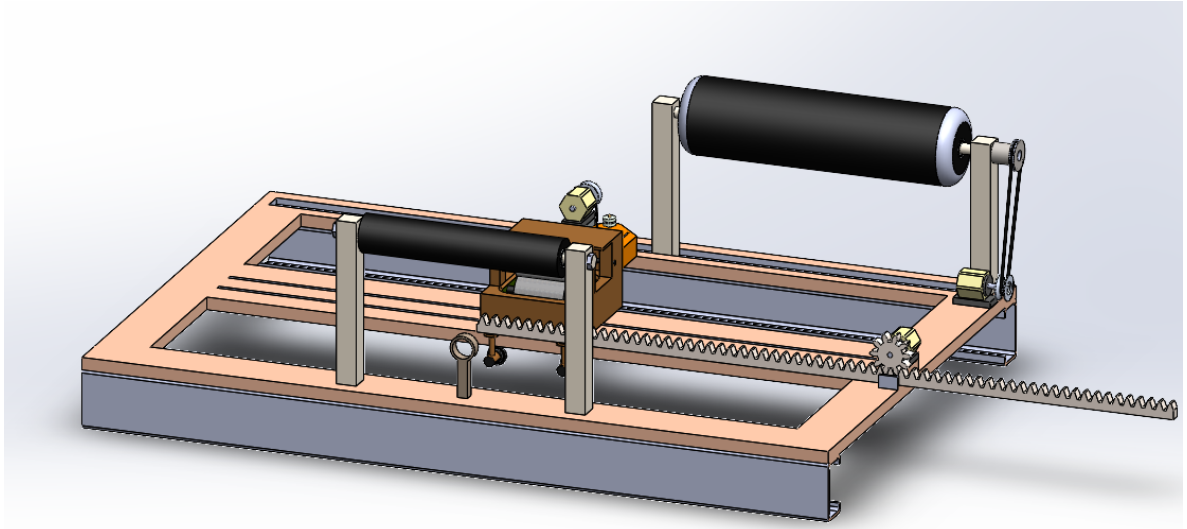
Máquina Filament Winding vista dimetrica. Autor
